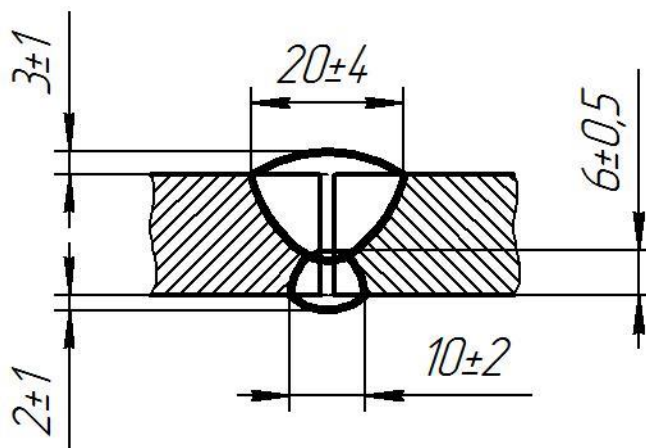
Геометрические параметры сварного шва после автоматической сварки в углекислом газе
